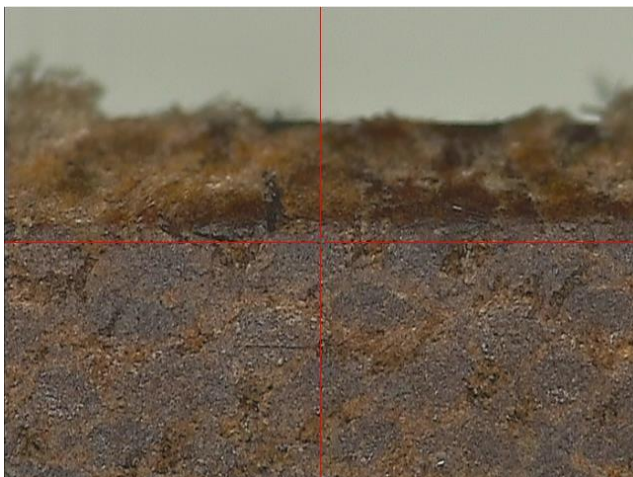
Профил на напречни сечения на маркировки получени върху образци от “ Inconel 718” [100]
